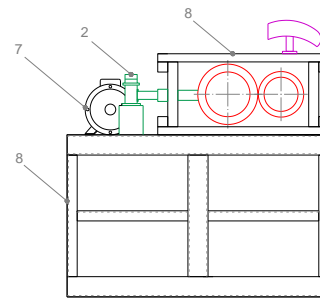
Diseño de forma de la Destalonadora, vista frontal
